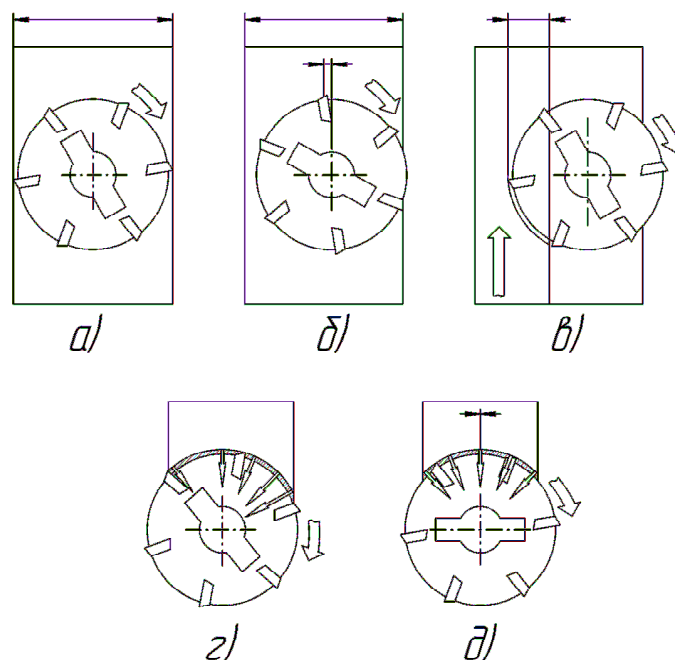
Взаимное расположение фрезы относительно оси заготовки
